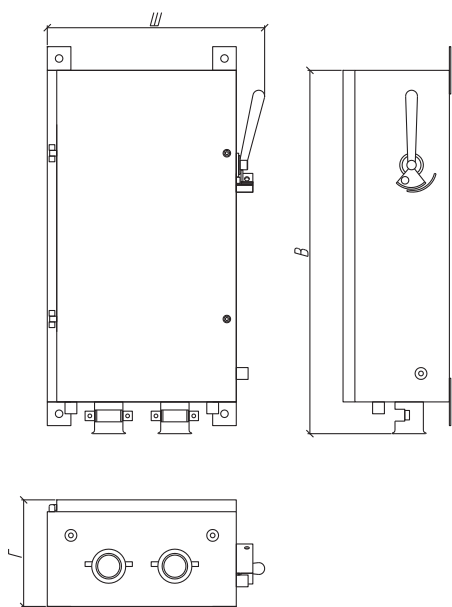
Выключатель автоматический рудничный постоянного тока ВАРП-500.
